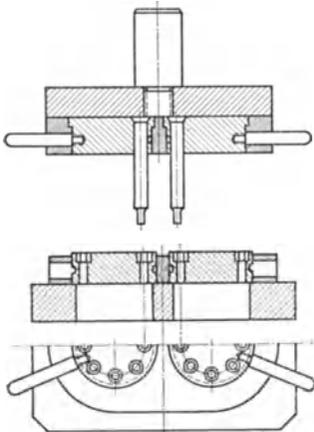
Drehbare Werkzeugbefestigung. (Nach Masch.-Bau 1936 S. 320).
